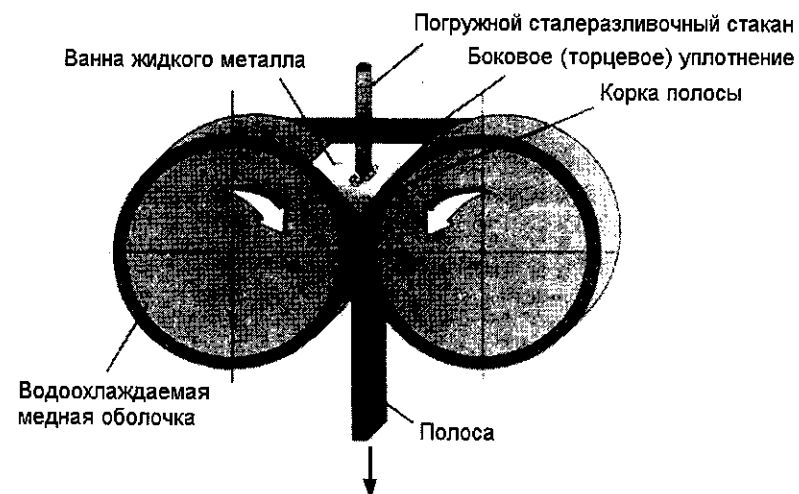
Схема формирования заготовки на двухвалковой МНЛЗ
